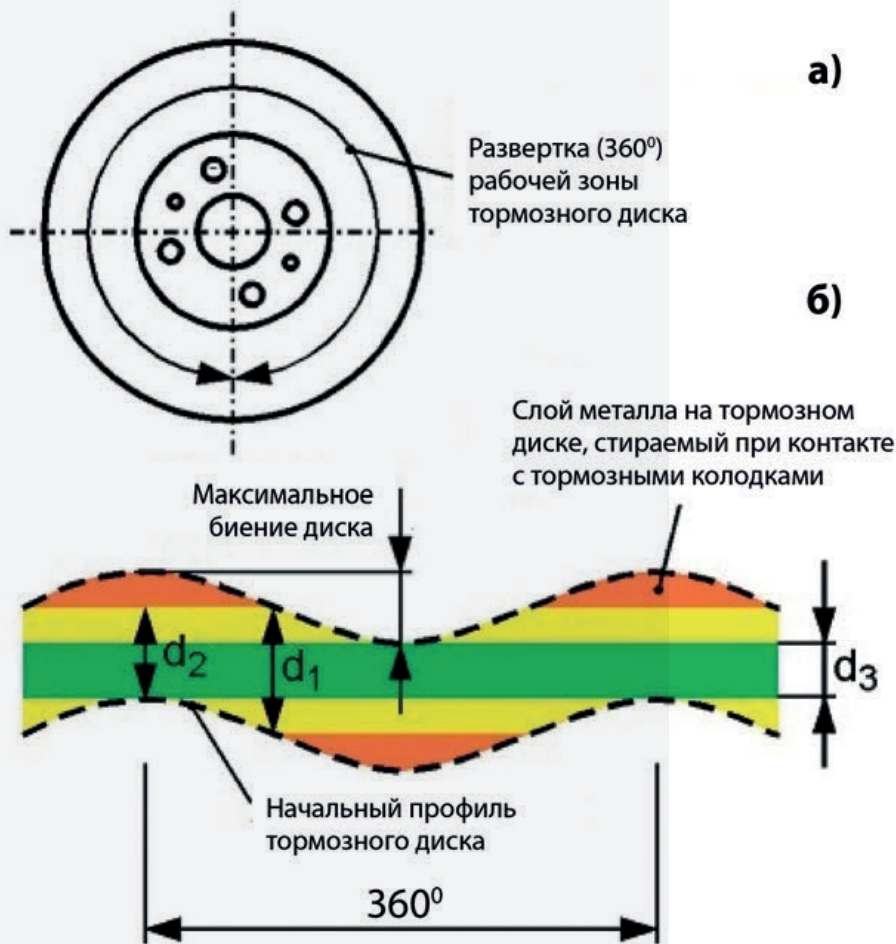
Эскиз развертки рабочей поверхности тормозного диска
